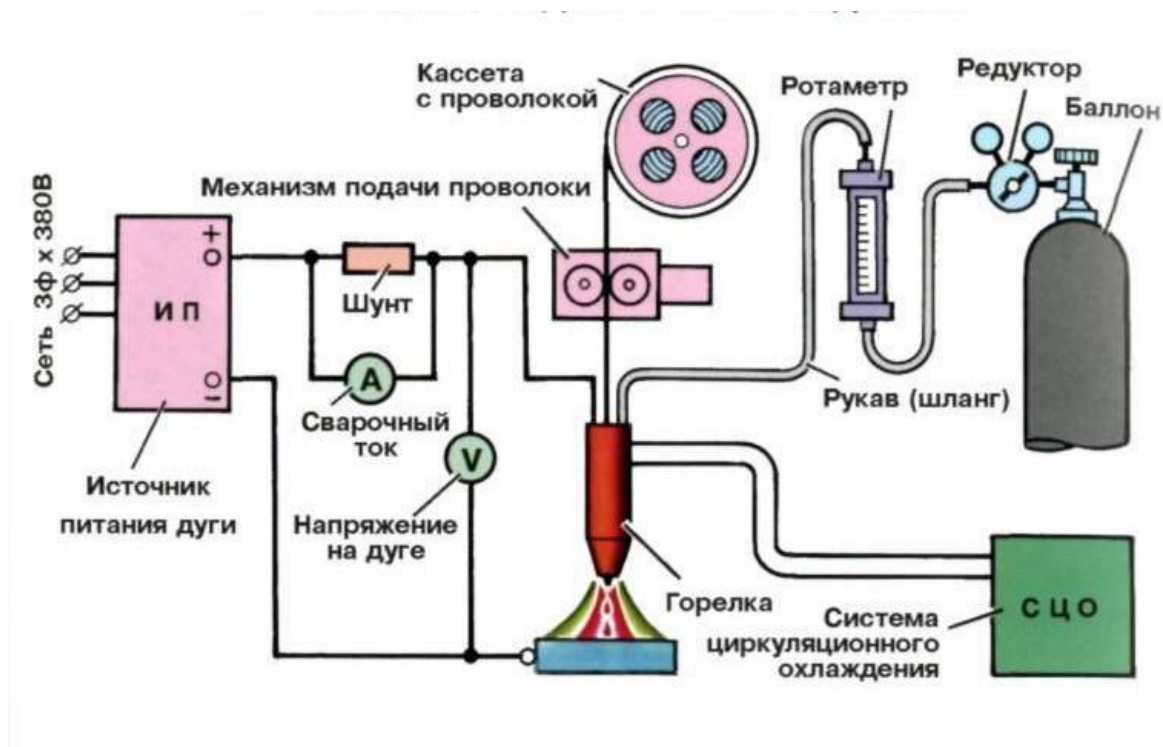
Установка для дугового наплавления у вуглекислому газі
